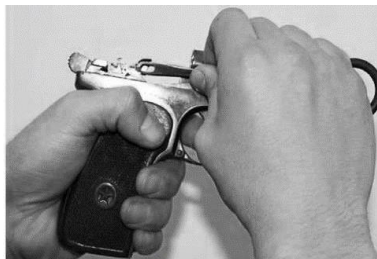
Снятие крючка пружины шептала с затворной задержки
